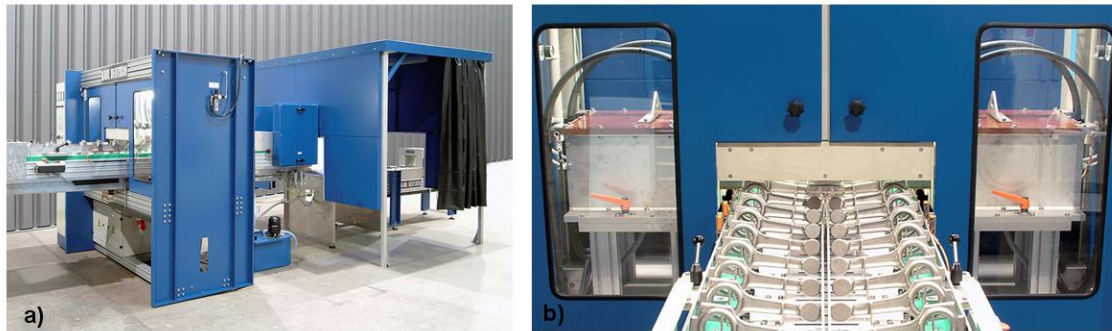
Bauteiltransport mit einem Kettenförderer, a) Seitenansicht der Prüflinie, b) Einlaufseite der Prüfmaschine.
